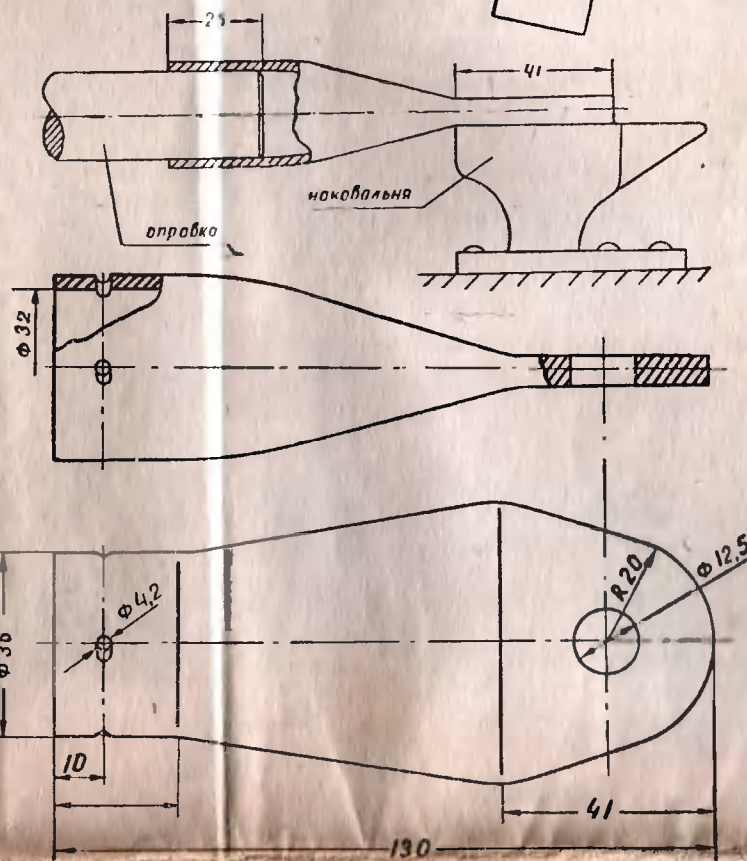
Обойма подшипника. Труба диаметром 32—36 мм. Сталь сечением 20 мм. Изготовленные обоймы подшипника
